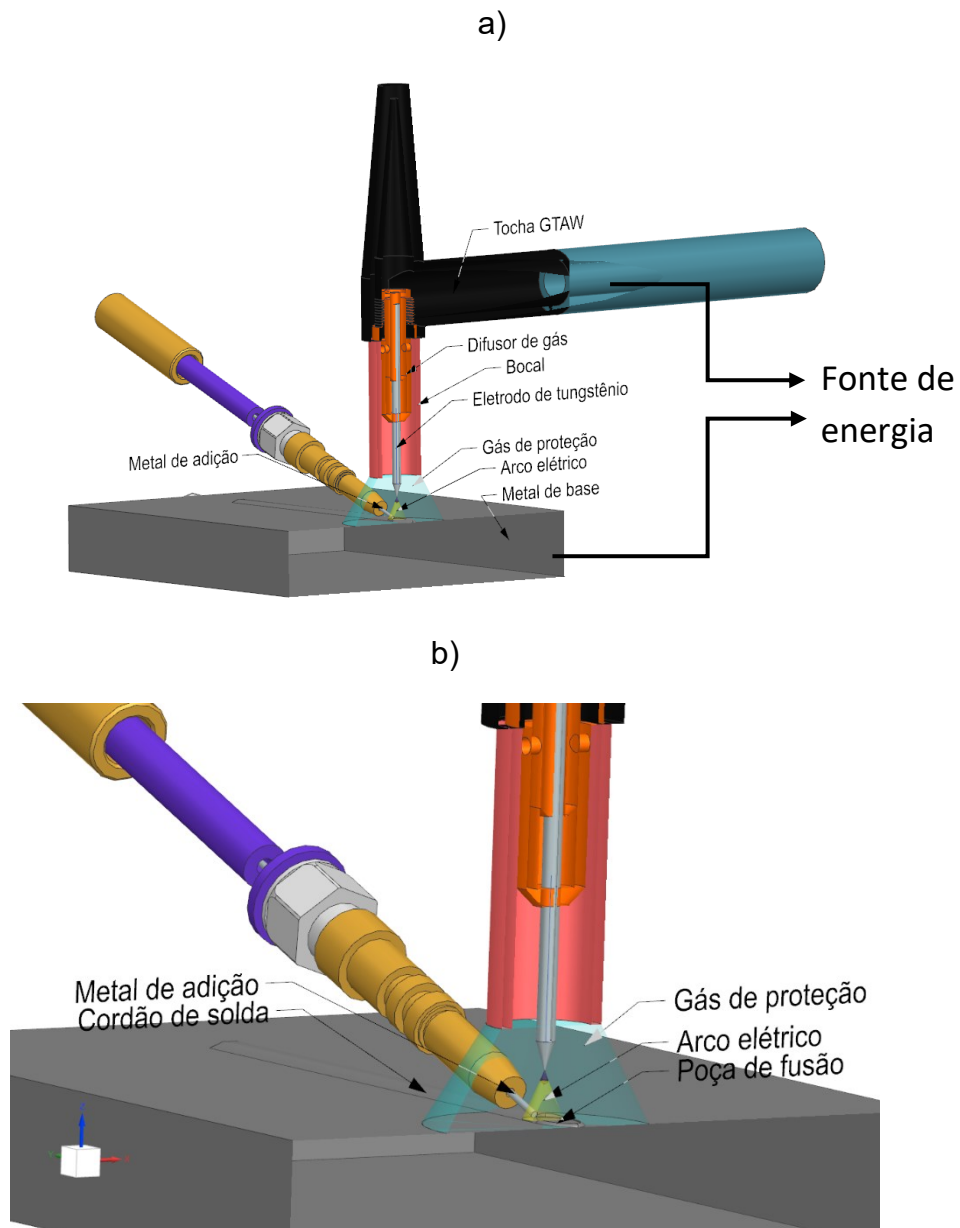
Processo de soldagem GTAW: a) Representação geral do processo, b) Representação ampliada do processo de soldagem.
